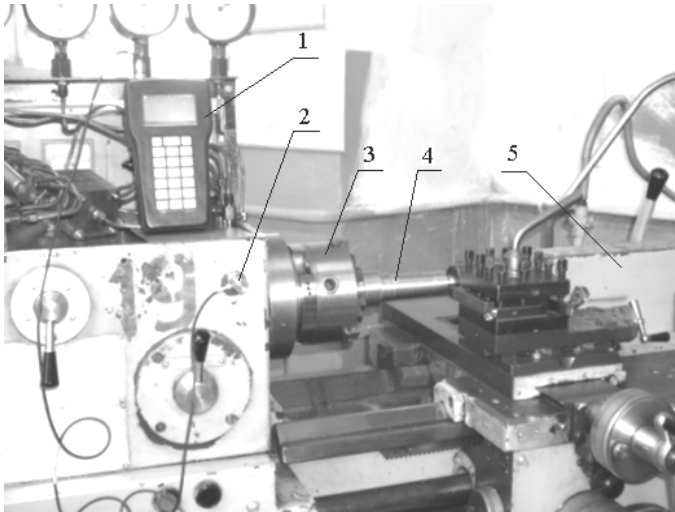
Загальний вигляд експериментальної установки на базі прецизійного токарно-гвинторізного верстата УТ61А: 1 - аналізатор спектра вібрацій 795М; 2 - акселерометр КД-41; 3 - патрон; 4 – оброблювана заготовка; 5 - задня бабка
